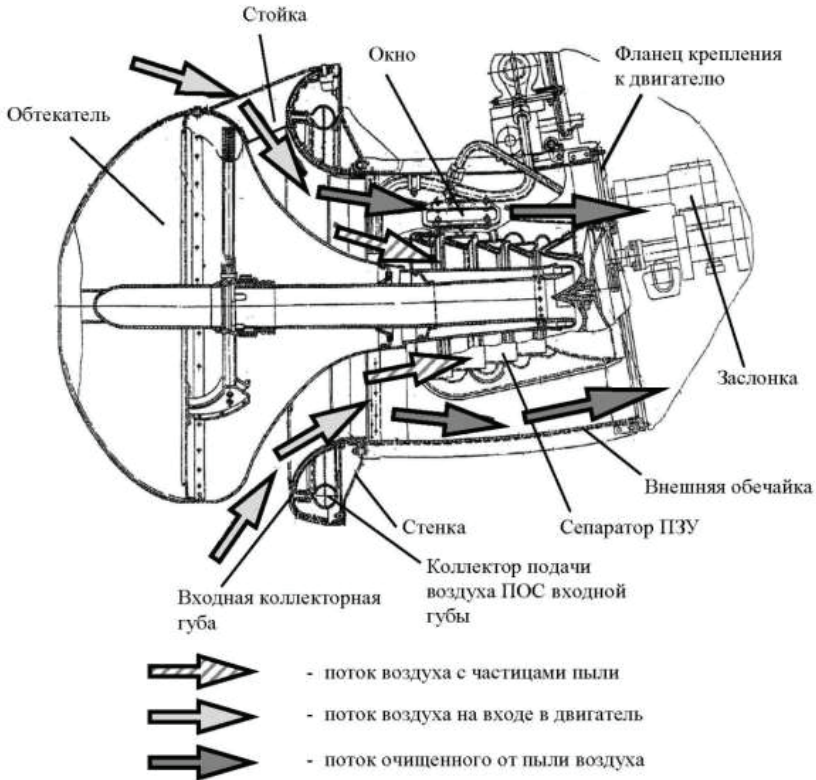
Пылезащитное устройство двигателя вертолета Ми-171
